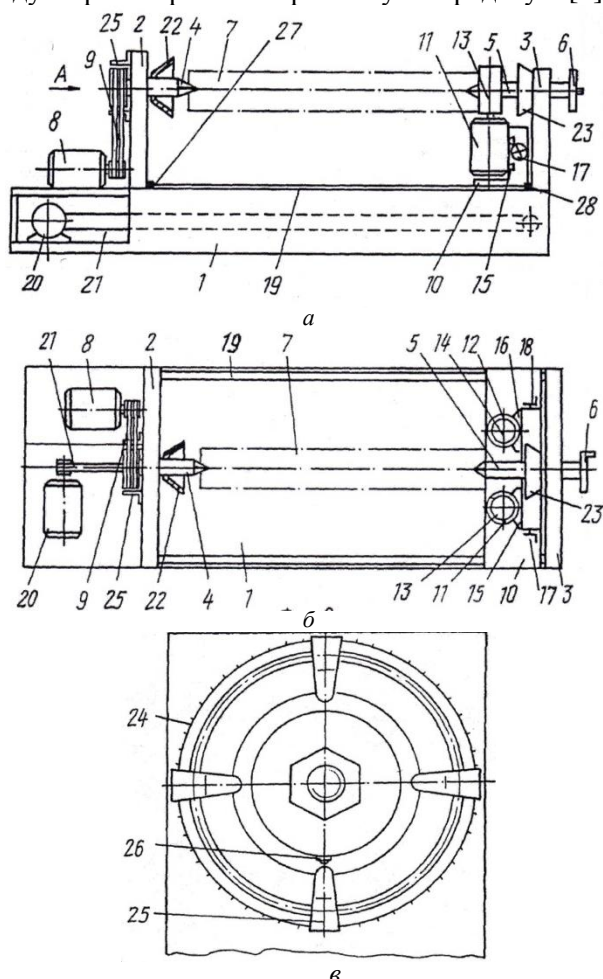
Схема станка для обработки бревен: а – вид спереди; б – вид сверху; в – вид А
